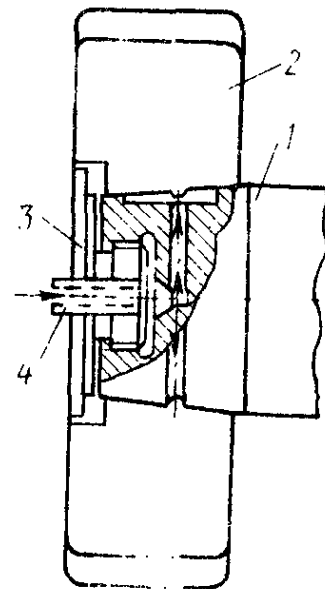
Схема подвода масла при гидравлическом съеме шестерни с вала тягового двигателя:
